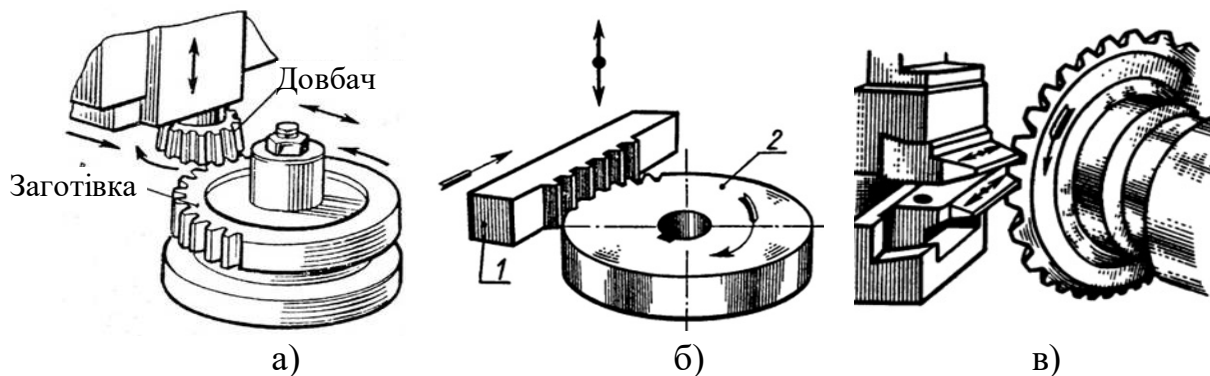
Нарізання зубів: а – довбачем; б – рейкою; в – різцями
